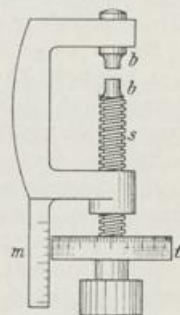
Schraubenlehre. (Mikrometerschraube.)
